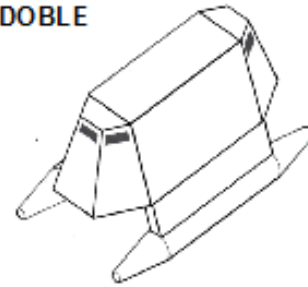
Práctica 21 Barco de doble casco, vista explosionada
